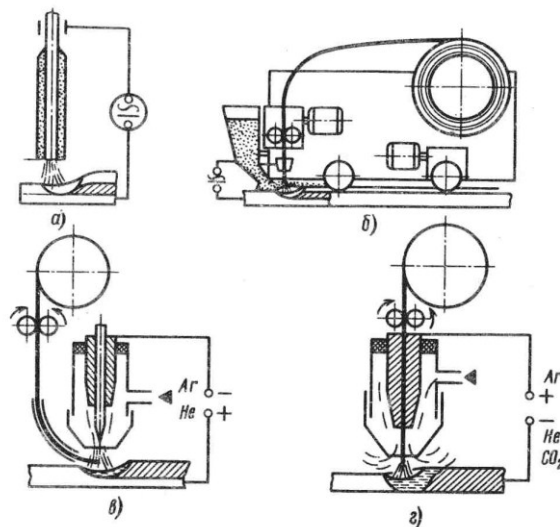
Дуговая сварка: а — ручная; б — автоматическая под флюсом; в — в защитных газах неплавящимся электродом; г — в защитных газах плавящимся электродом
